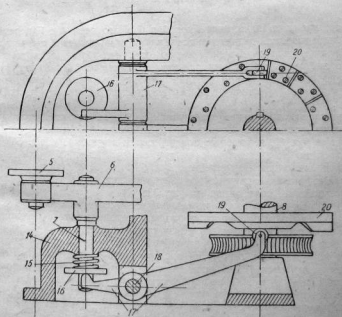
Схема копирующе-фрезерного автомата Гаузер.
